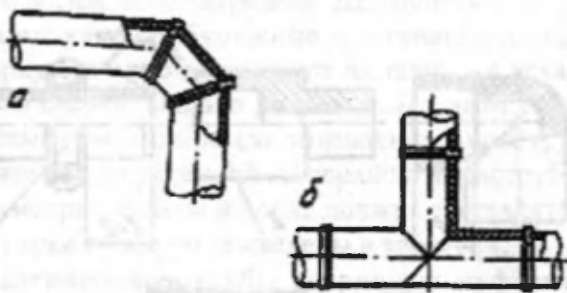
Сварные стыковые соединения труб со сварными соединительными деталями:
